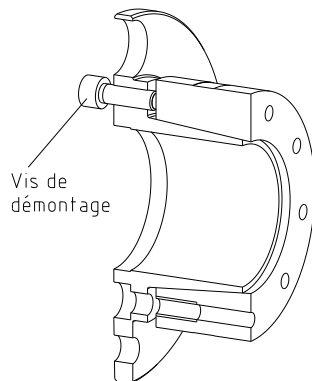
Démontage du moyeu à frette de serrage 6.0
